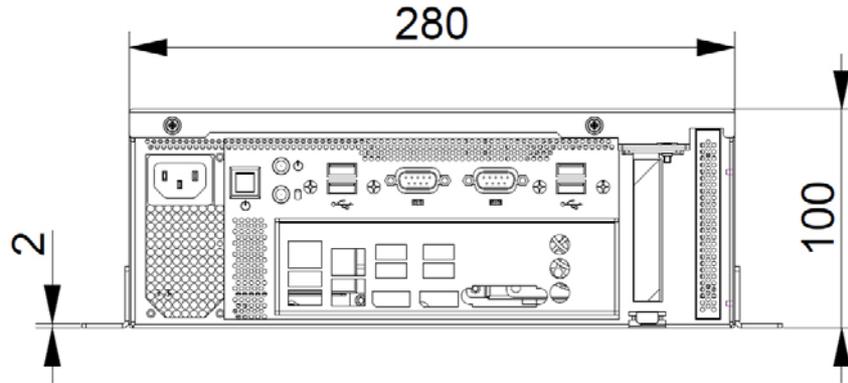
Maßangaben in der Frontansicht (Tischmontage)
